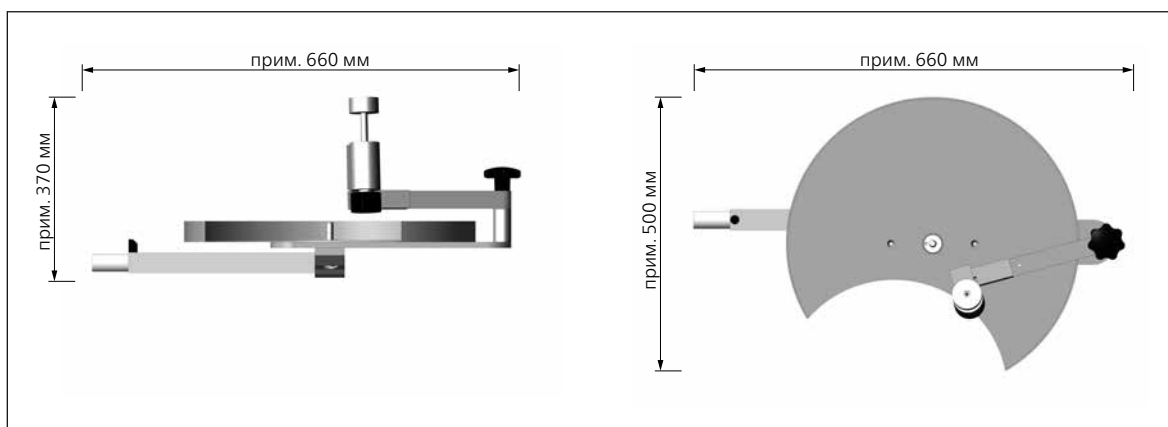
Размеры в мм (HV 205-2, вид спереди/вид сверху)
